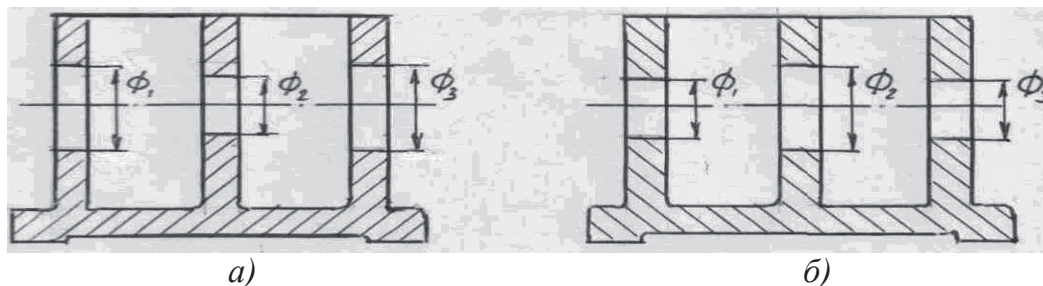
Корпусные детали с различными диаметральными размерами соосных отверстий на внутренних и наружных стенках: *а* – технологичные; *б* – нетехнологичные
